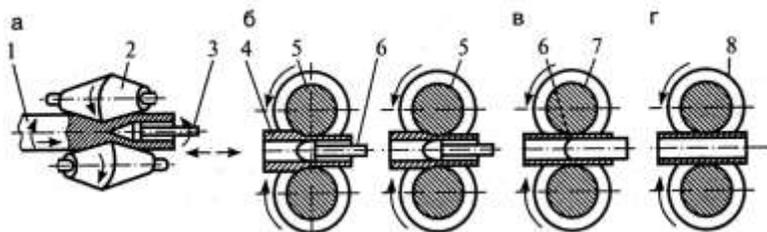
Схема прокатки бесшовных труб на трубопрокатной установке с автоматическим станом: а – прошивной стан; б – автоматический стан; в – обкатной стан; г – калибровочный стан; 1 – заготовка; 2 – валки; 3 – игла; 4 – труба; 5 – круглые калибры; 6 – оправка; 7 – обкатные валки; 8 – калибровочные валки
